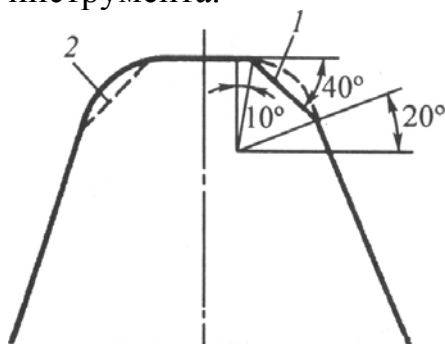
Прогрессивная схема резания со стружкоразделительными фасками на вершине зуба
